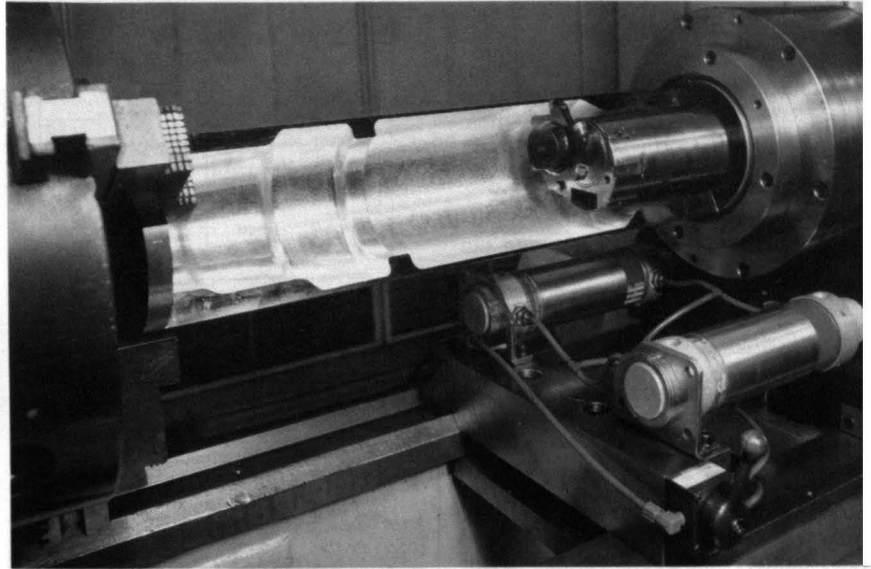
Versuchsmaschine mit Auskammerfräsbohrwerkzeug
